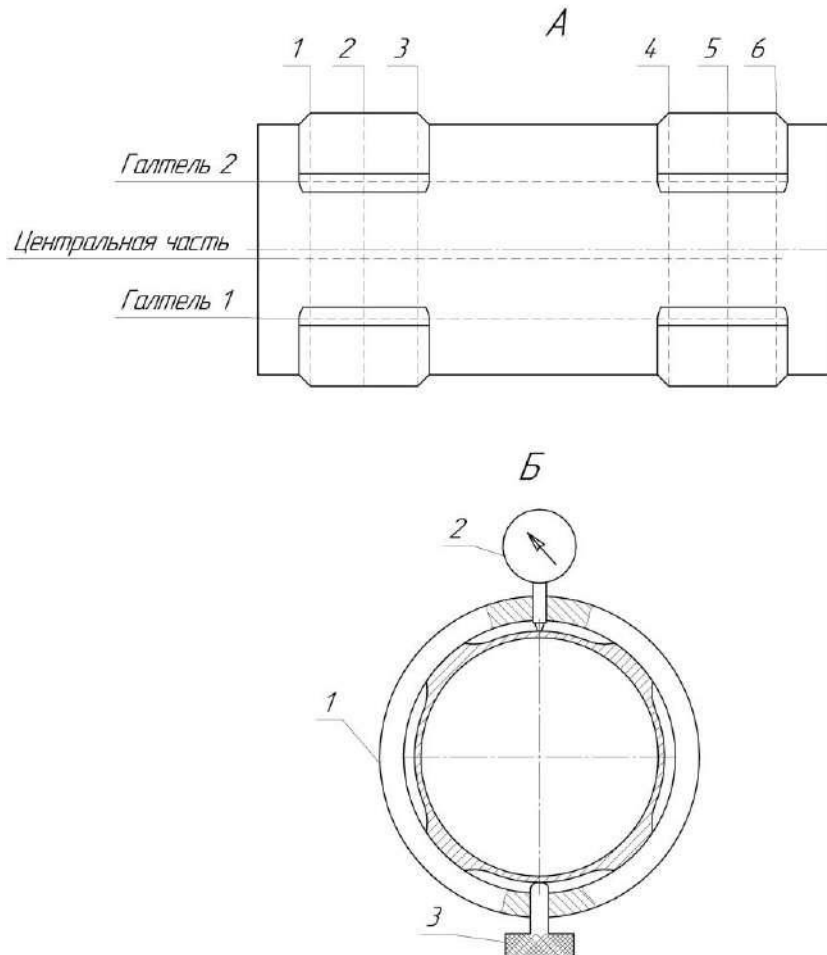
Схемы замеров радиусов фрезерованной поверхности впадин втулки
